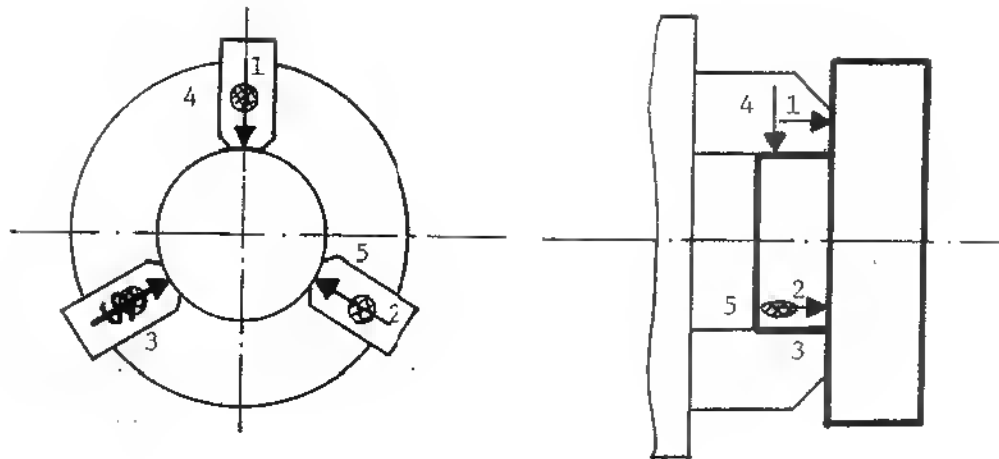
Serrage et positionnement d'une pièce cylindrique courte sur mandrin trois mors. Appui plan et centrage court avec serrage.
